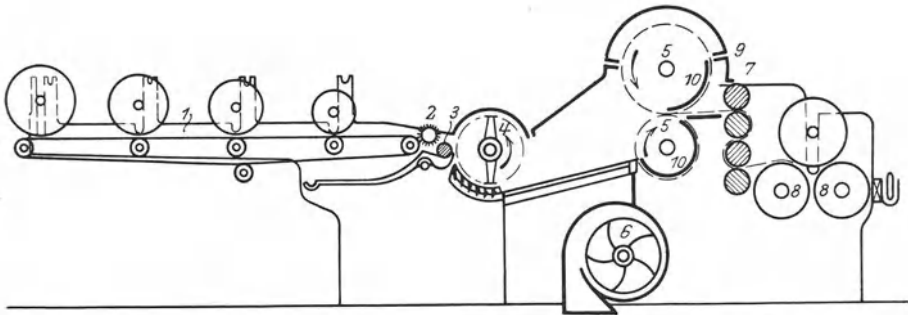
Einfache Schlagmaschine. Längsschnitt.
